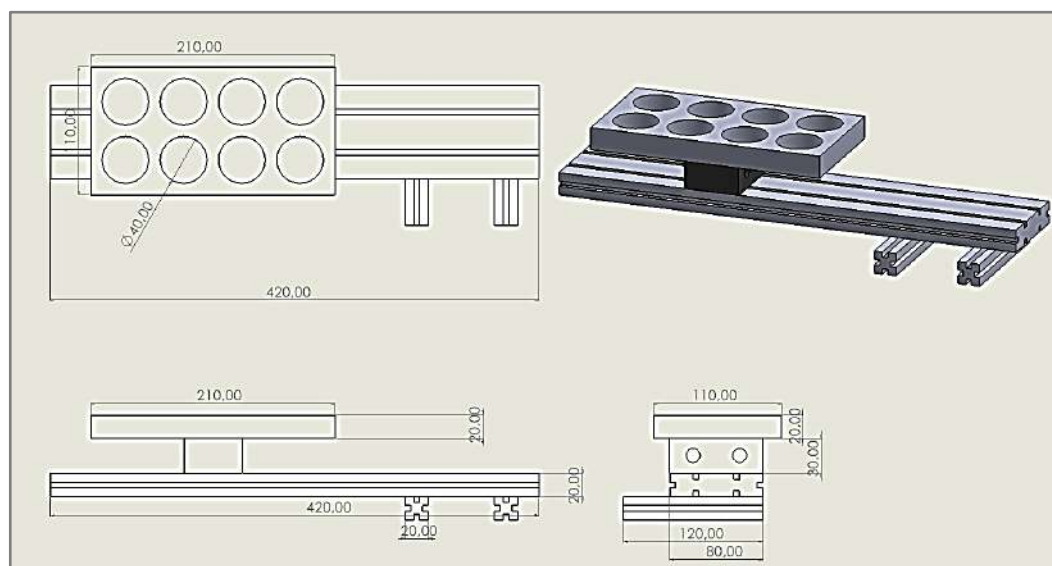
Plano estructural almacén de componentes neumáticos
